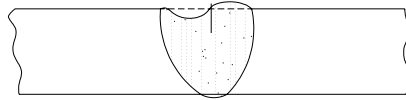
Deposição insuficiente de metal de solda em junta de topo.
